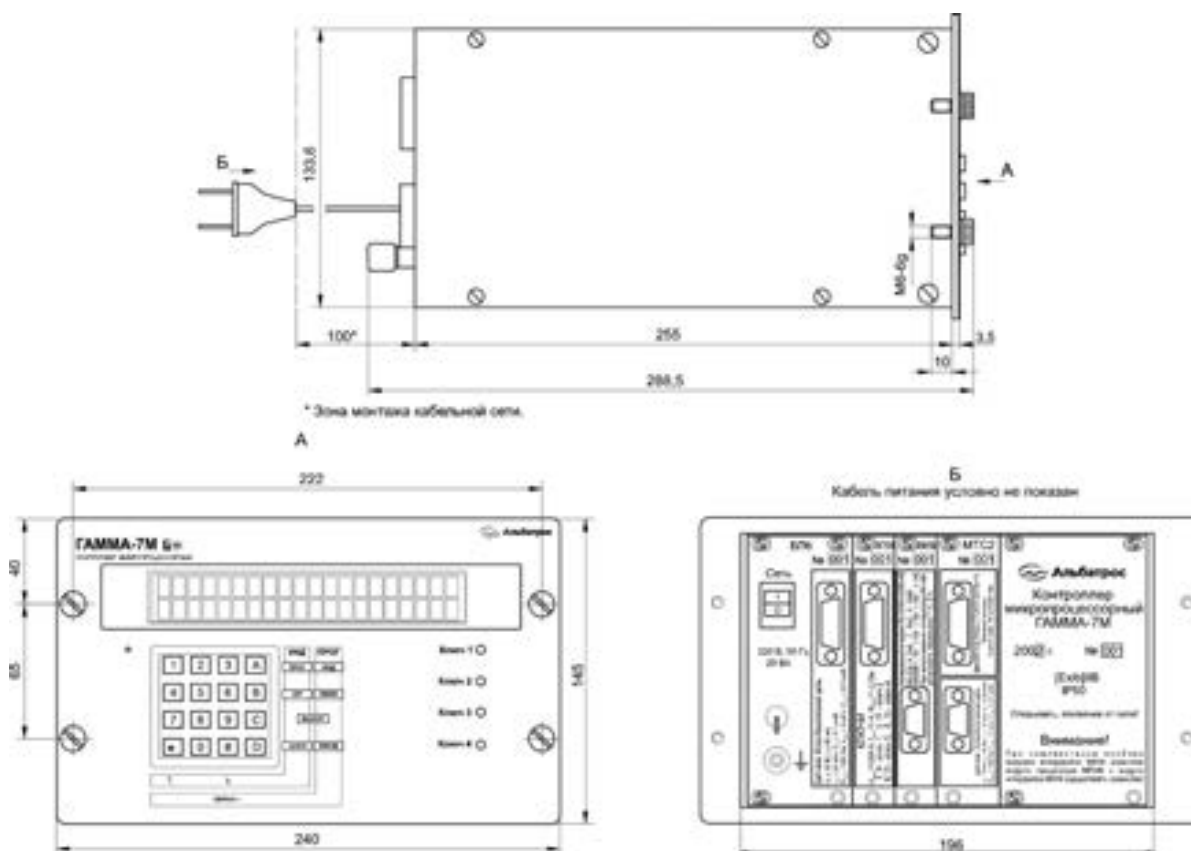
Внешний вид и габаритные размеры прибора (на примере исполнения 7)
